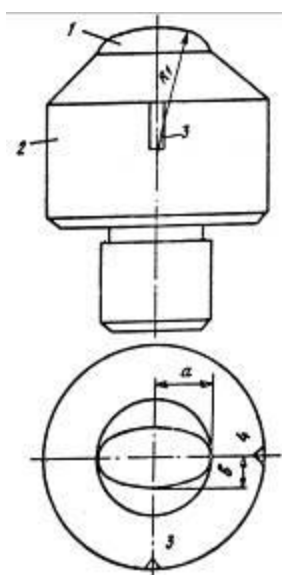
Инструмент с криволинейной формой заточки
